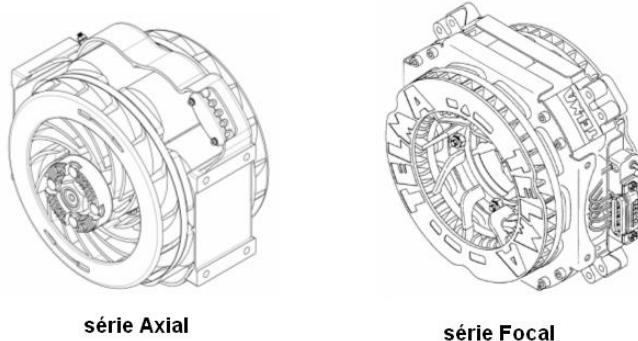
Chlazení retardéru pomocí lopatek rotoru [9]
